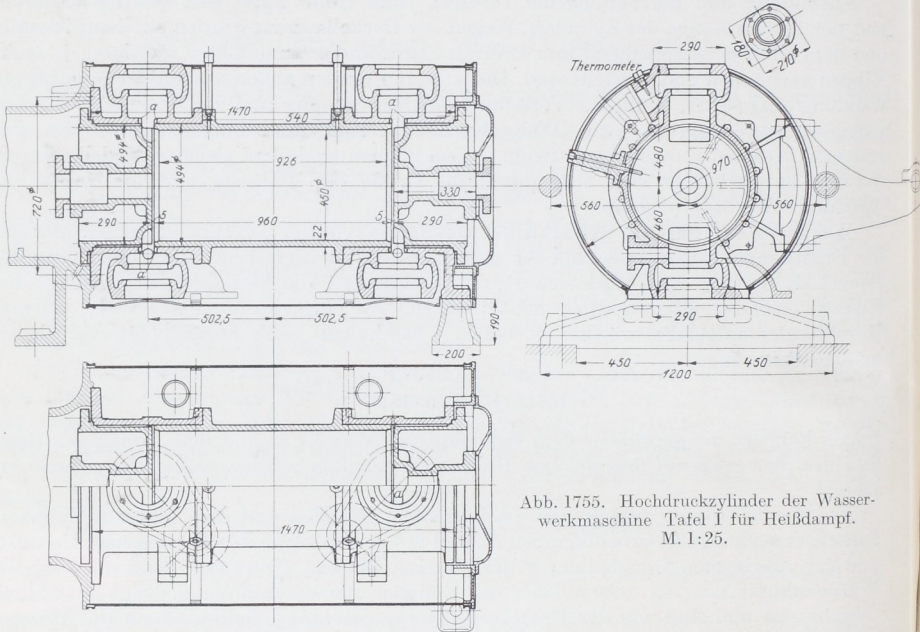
Hochdruckzylinder der Wasserwerkmaschine Tafel I für Heißdampf.
